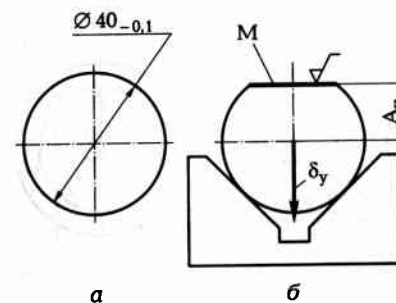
Схема установки заготовки (a) на призму при фрезеровании ($б$) плоскости
